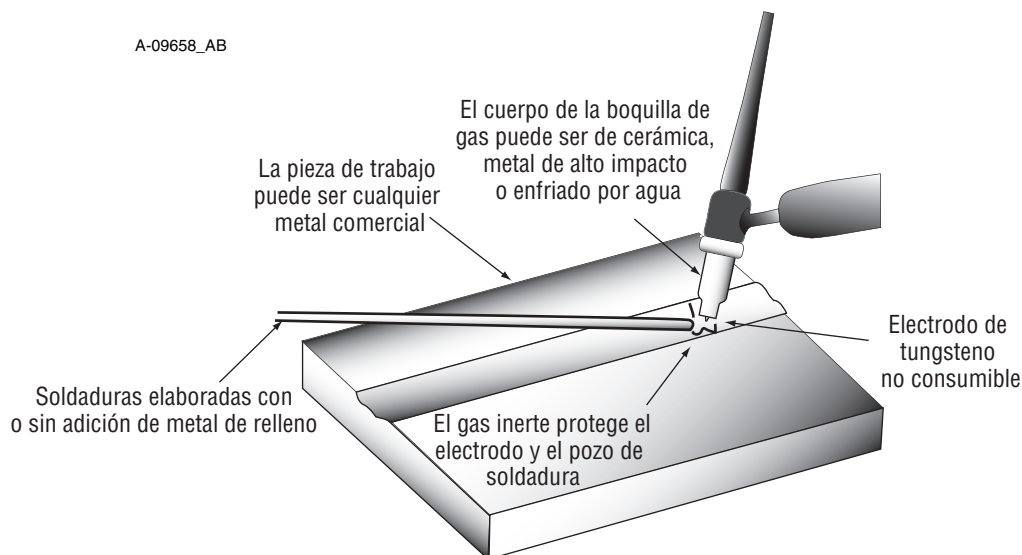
Esquema de la aplicación de la soldadura TIG (GTAW)
